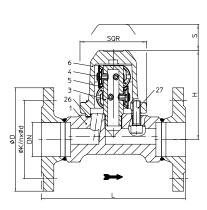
1....6K2 (DN40-50) mit 6 Kapseln, mit Flanschen
